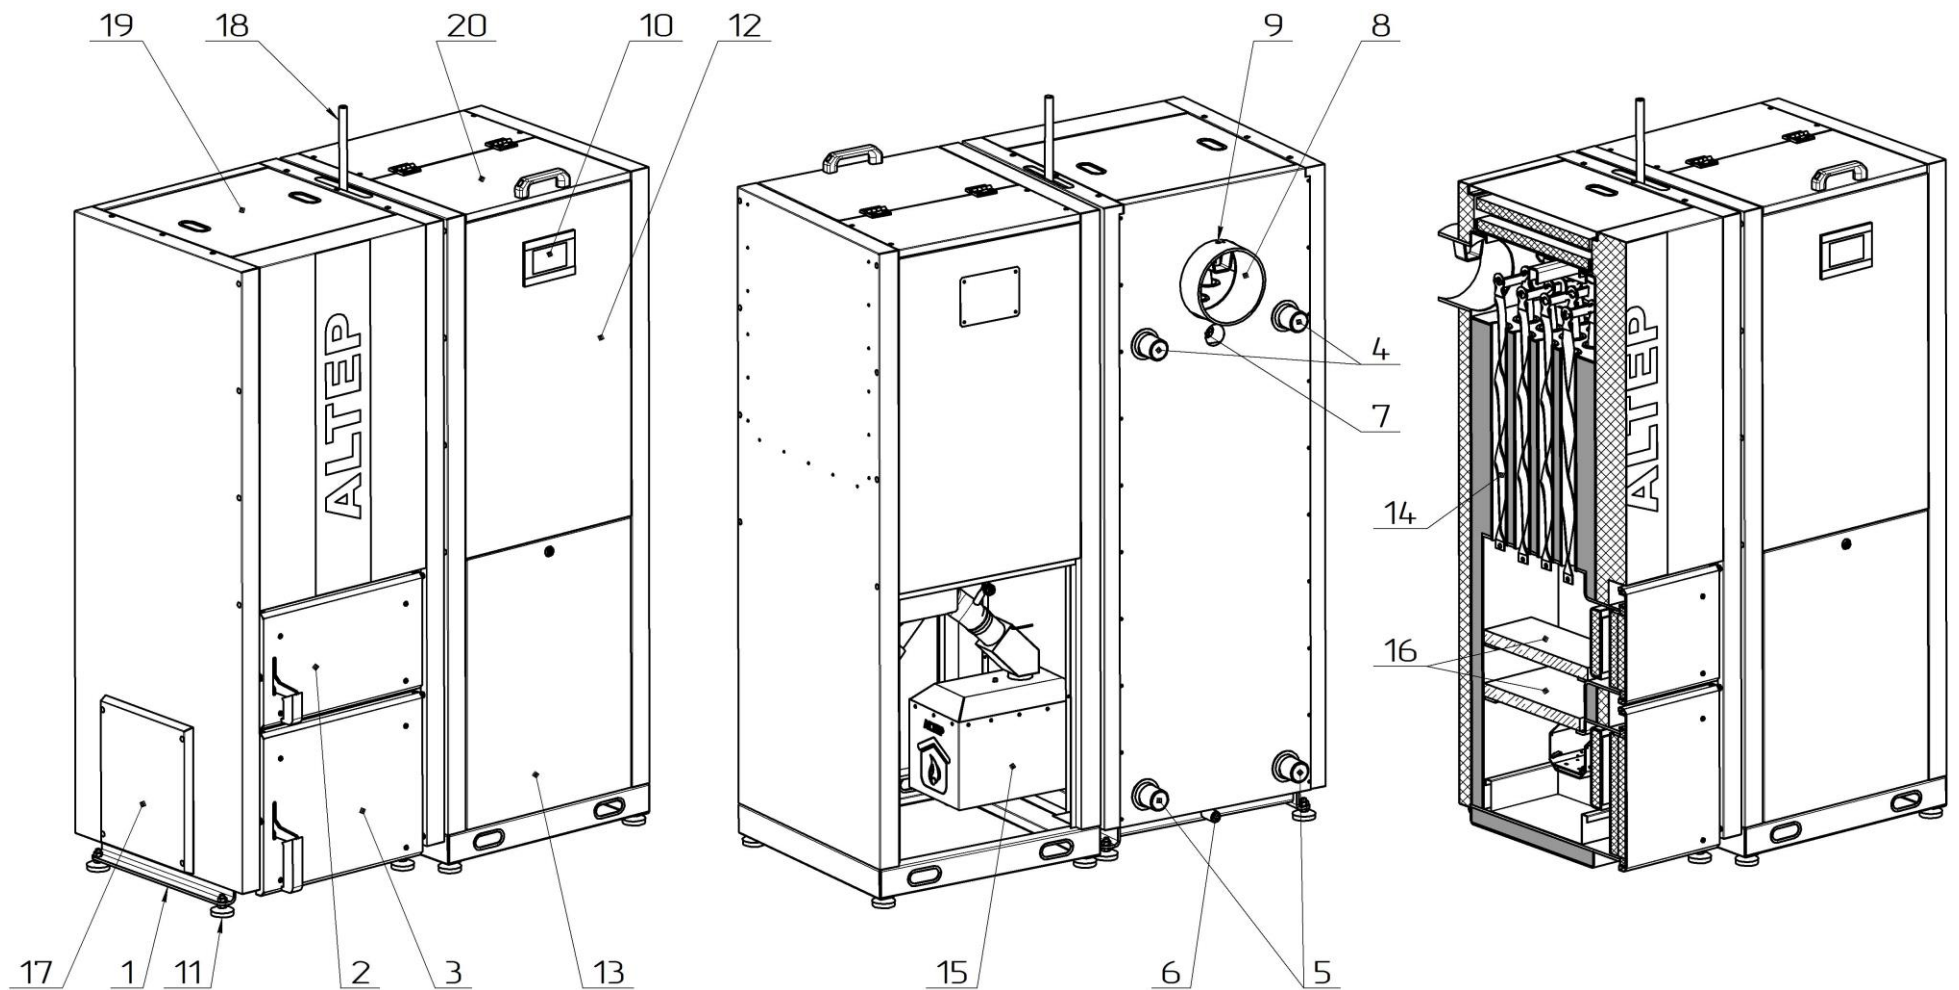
Габаритне креслення котла типу A-Pellets
